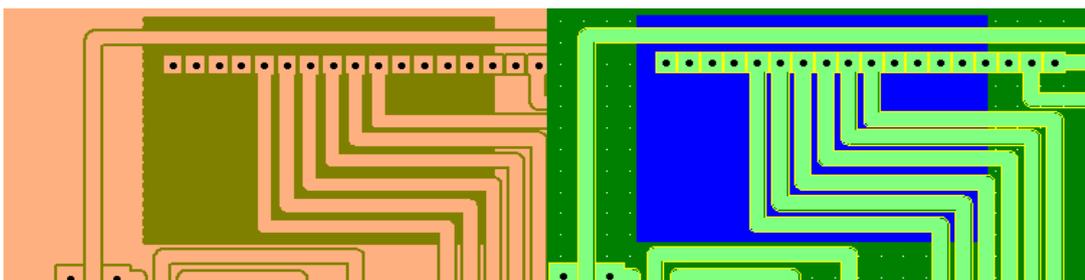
Parte final del engrava miento del circuito electrónico.
